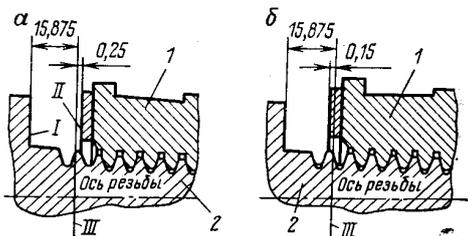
Схема проверки внутренней замковой резьбы по ГОСТ 5286—75 калибрами:
